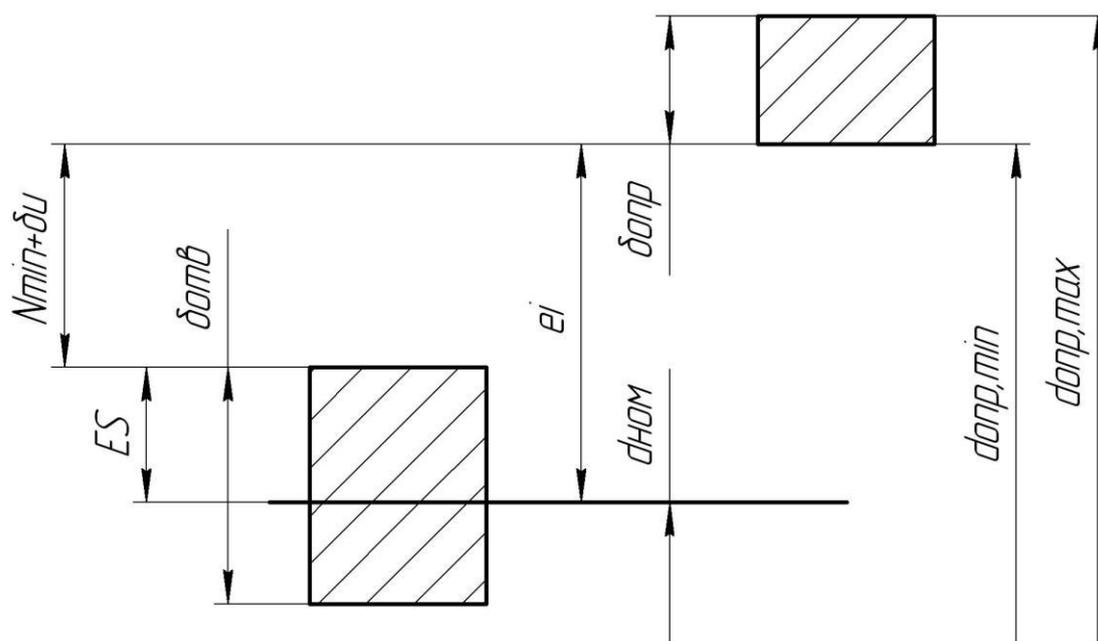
Схема взаимного расположения полей допусков оправки и заготовки
